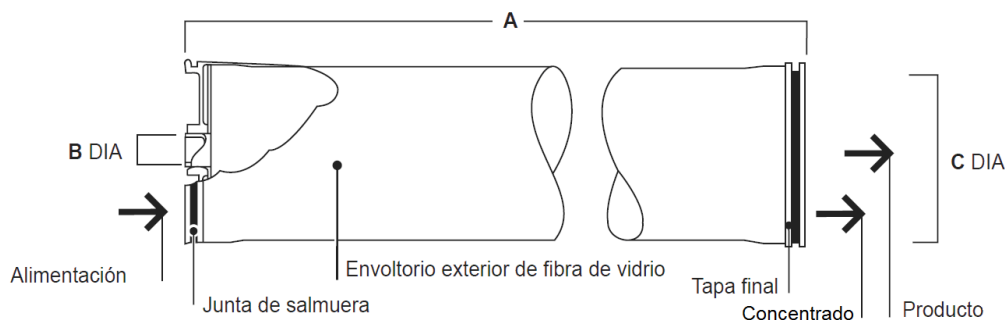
Elemento FILMTEC™ BW30-400 del sistema de ósmosis inversa instalado en Planta San Pedro.
